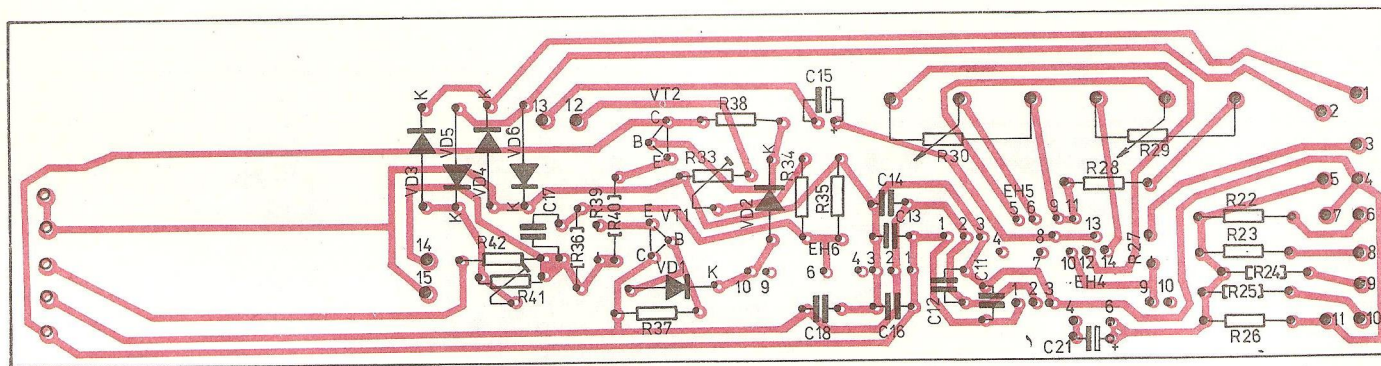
Deska směšovací 3AK 061 39 (strana součástek)
